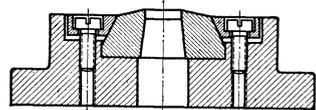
Befestigung der Schnittplatte durch Schräge und Druckstück.
